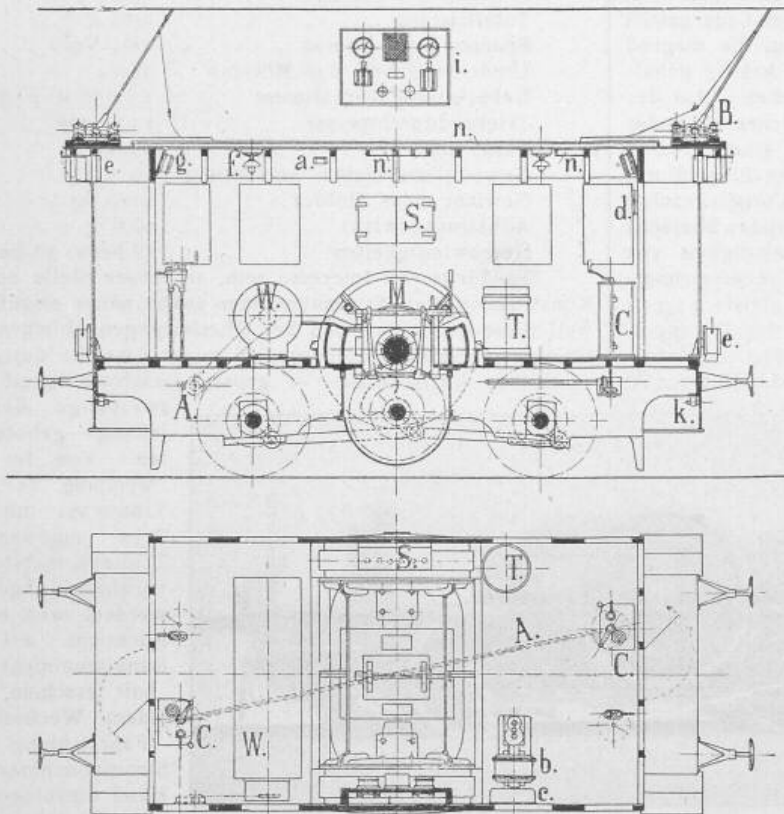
u. 35. Längsschnitt und Grundriss. 1:75.
